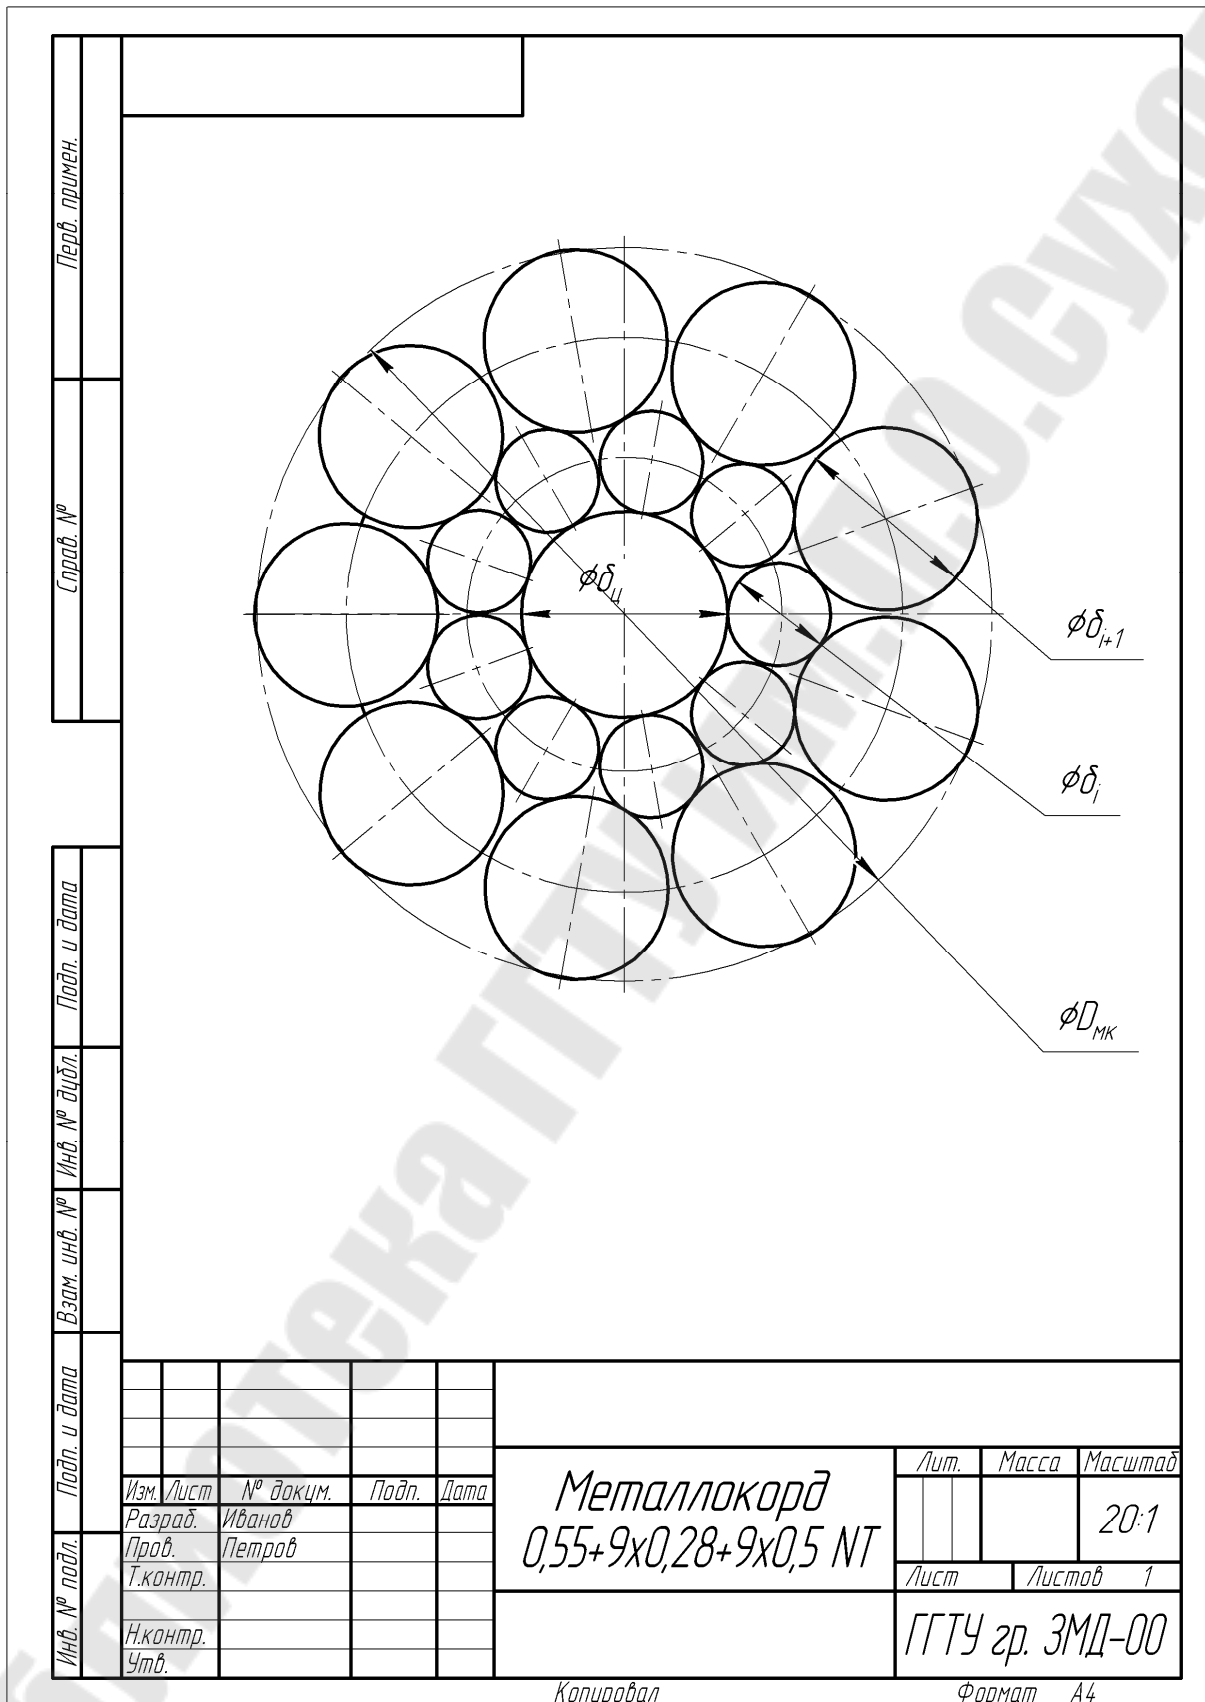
Пример оформления чертежа поперечного сечения металлокорда
